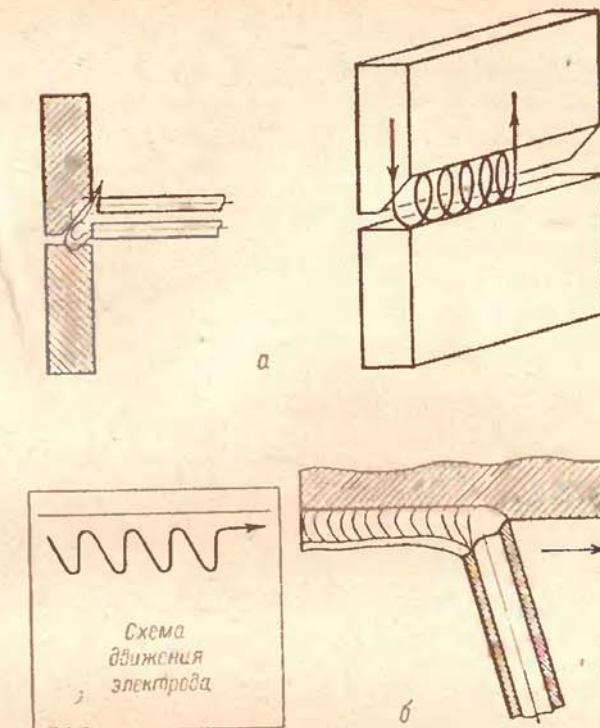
Сварка швов в различных пространственных положениях:
